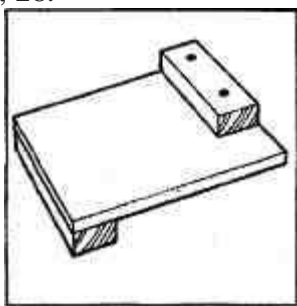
Куска столярной плиты и двух кусков планки достаточно для изготовления практической цулагы.
